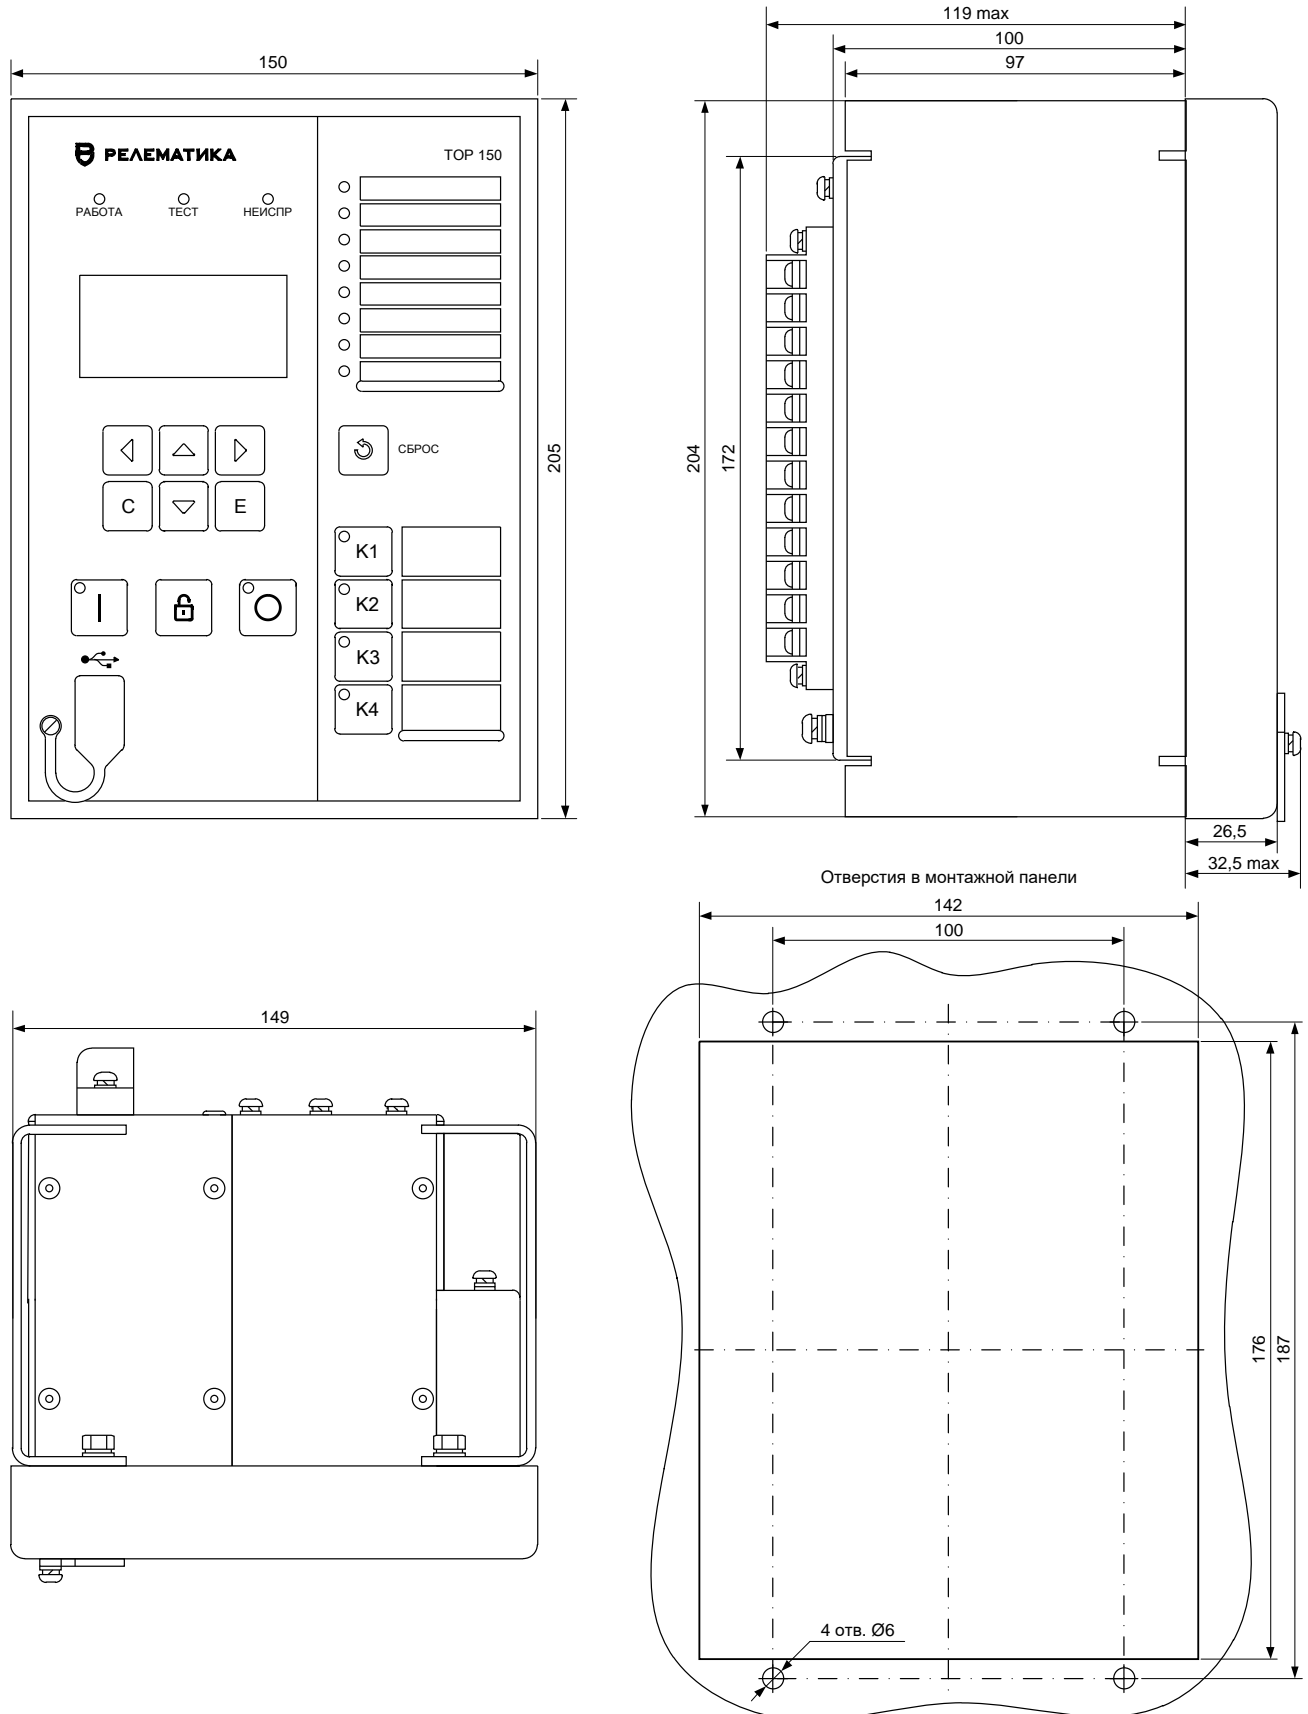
Габаритные и установочные размеры устройства TOP 150 с КМЧ 011-00
